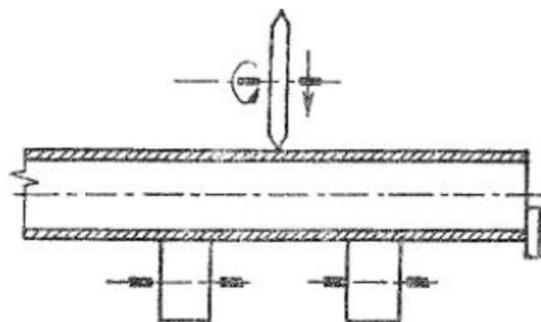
Schéma stříhání tenkostěnných trubek horizontálně-vertikálním způsobem [3]
